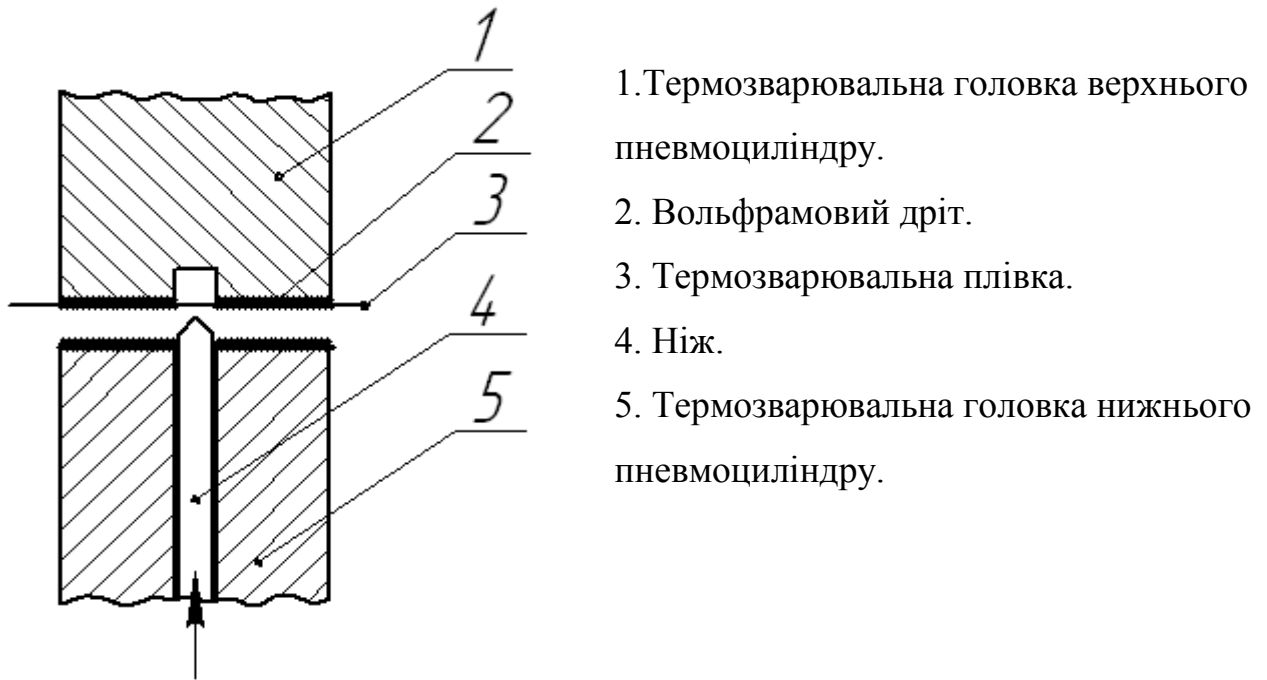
Пристрій для поперечного зварювання плівки.
